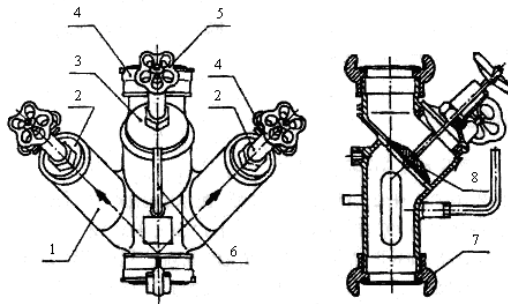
Будова розгалуження рукавного триходового: 1 — корпус; 2 – перекриваючий пристрій бокового вихідного патрубку; 3 — перекриваючий пристрій центрального вихідного патрубку; 4 — з'єднувальна головка на вихідному патрубку; 5 — маховичок; 6 — ручка; 7 — з'єднувальна головка на вхідному патрубку; 8 — затворний клапан
